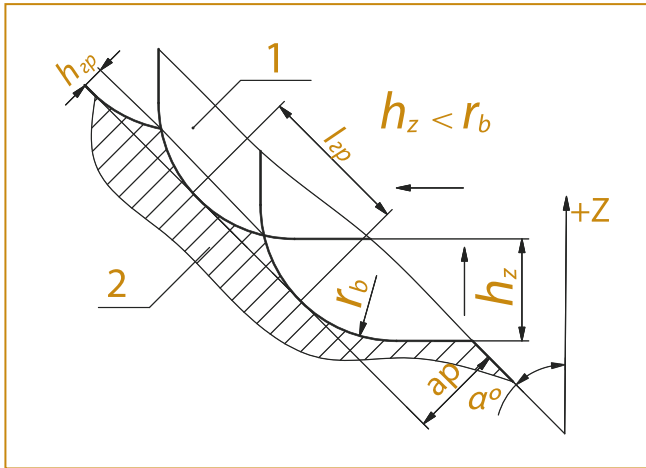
Вид и условные обозначения параметров «гребешка» на наклонной поверхности после 2,5-координатного фрезерования, где 1 – контур режущей части фрезы; 2 – заготовка;  $h_{zp}$  – высота гребешка;  $r_b$  – радиус при вершине режущего инструмента;  $l_{gp}$  – длина основания гребешка;  $a_p$  – глубина резания
